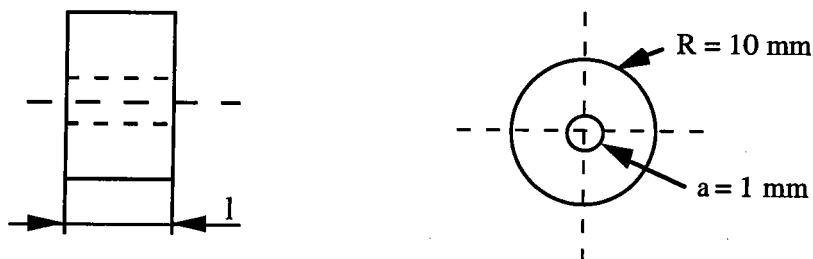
Géométrie des éprouvettes de compression latérale
